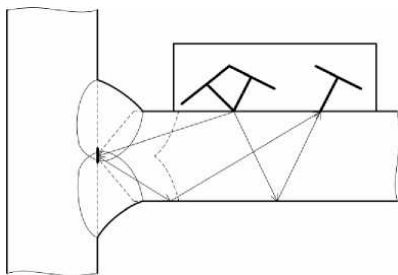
Схема контроля тавровых сварных соединений специализированным преобразователем СП5-75КУБ.
